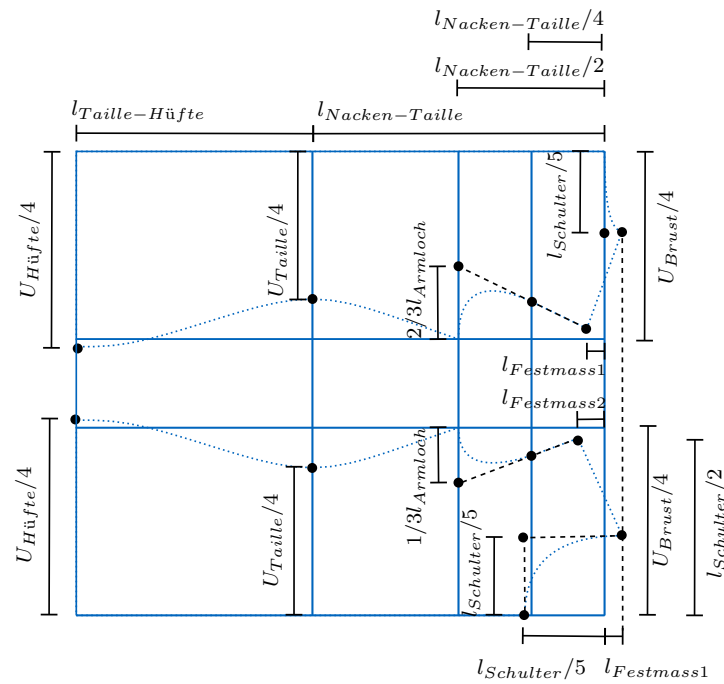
Parametrisierter Grundschnitt mit Rundhalsausschnitt des Damenoberteils anhand von Körpermaßen, Konstruktionsmaßen und Festmaßen.
